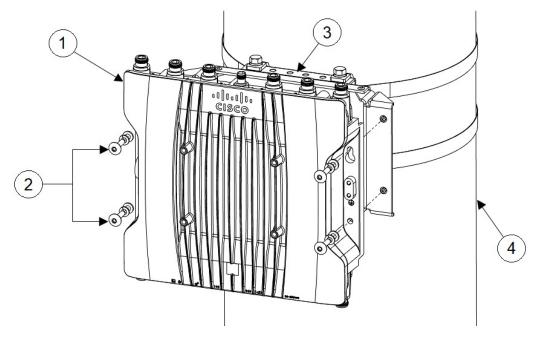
Suporte de montagem e conjunto de suporte de braçadeira em poste
